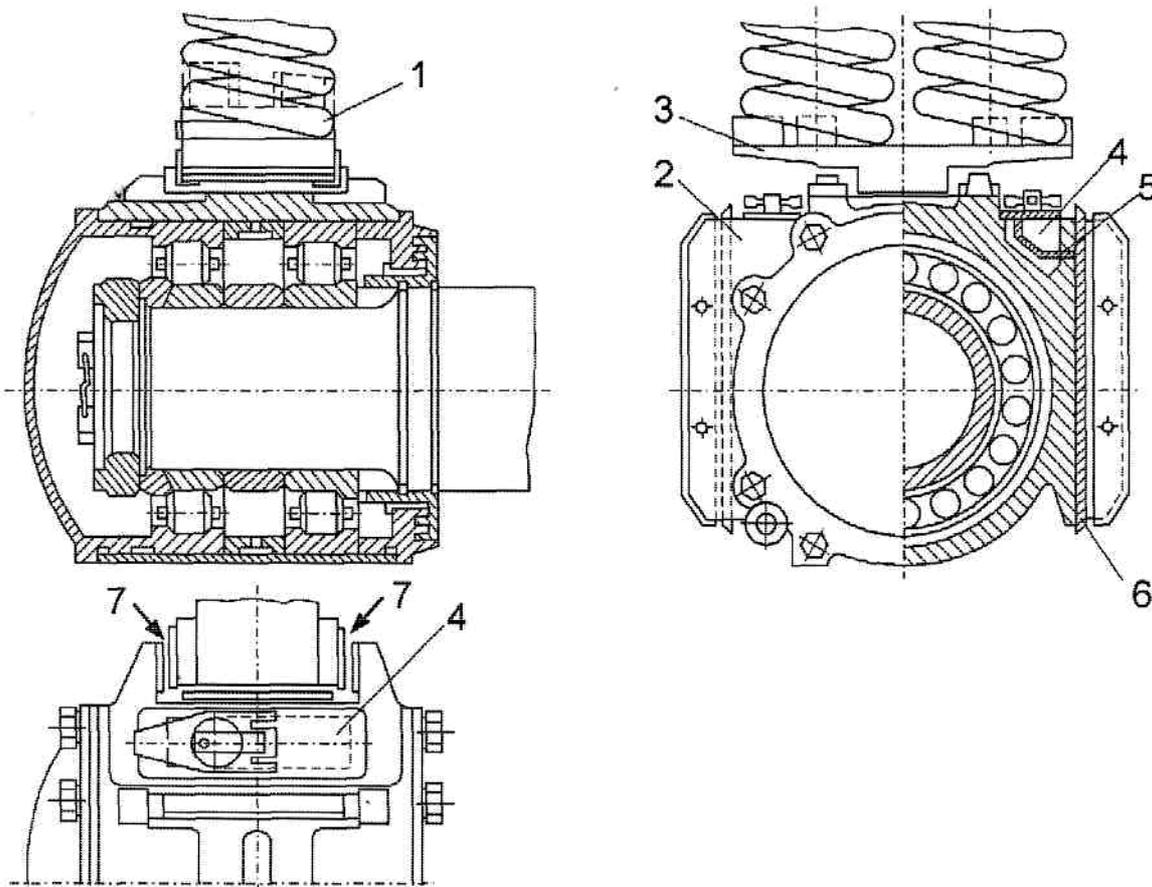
Челюстной буксовый узел электровоза ВЛ8: 1-комплект пружин; 2-корпус буксы; 3-опора; 4-резервуар для жидкой смазки; 5- фитиль для подачи смазки; 6,7-термообработанные сменные наличники;
